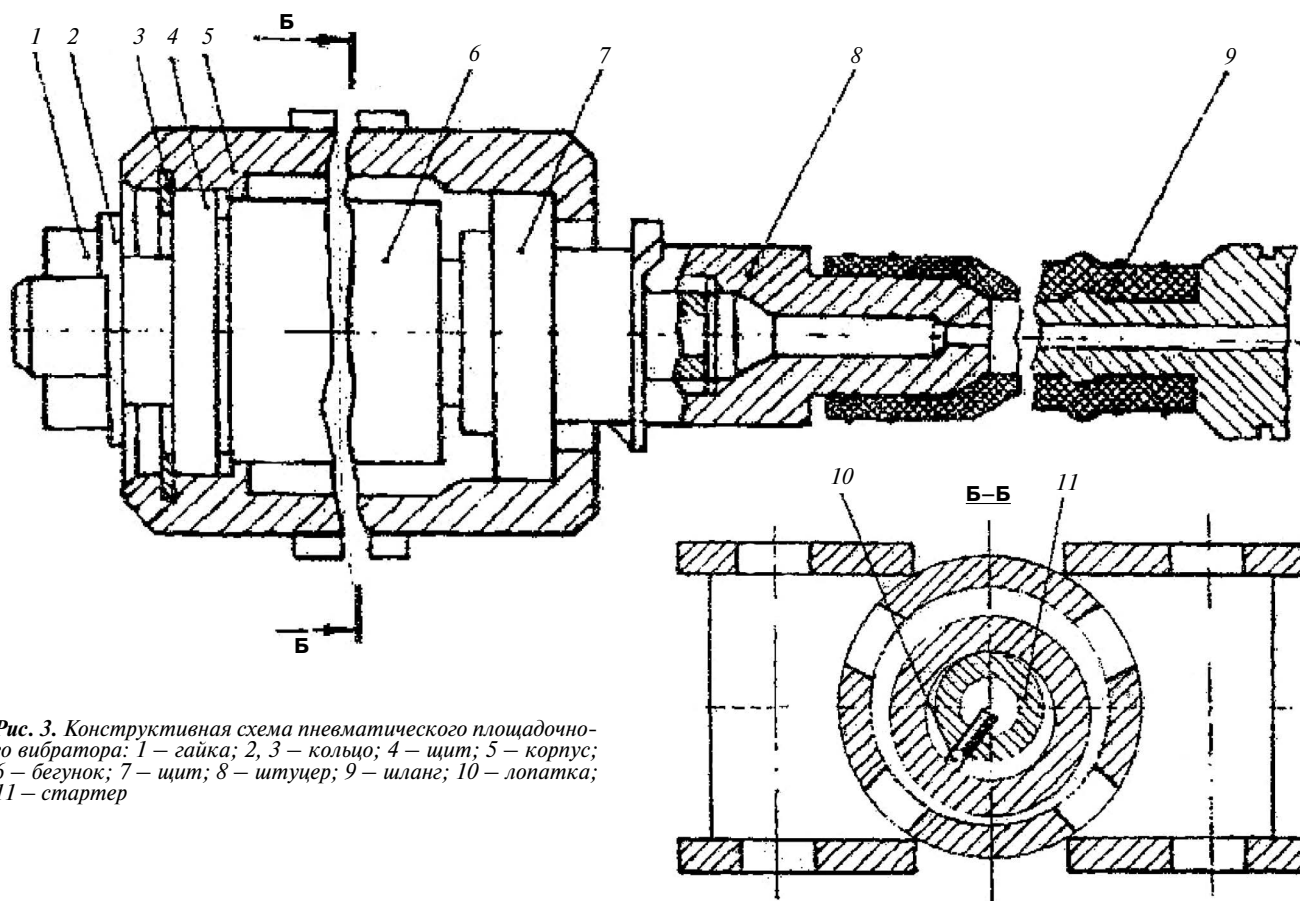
Конструктивная схема пневматического площадного вибратора: 1 – гайка; 2, 3 – кольцо; 4 – щит; 5 – корпус; 6 – бегунок; 7 – щит; 8 – штуцер; 9 – шланг; 10 – лопатка; 11 – стартер
